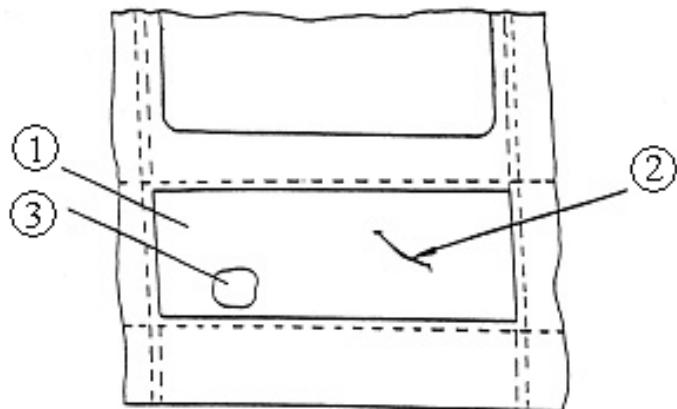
Дефекты металлической обшивки стен, ремонтируемые сваркой
